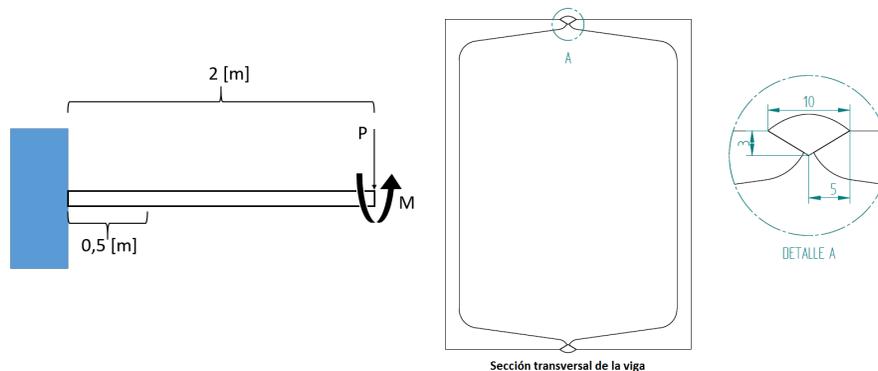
Sección de la viga y aplicación de la fuerza y momento. En el detalle A las cotas están en mm
